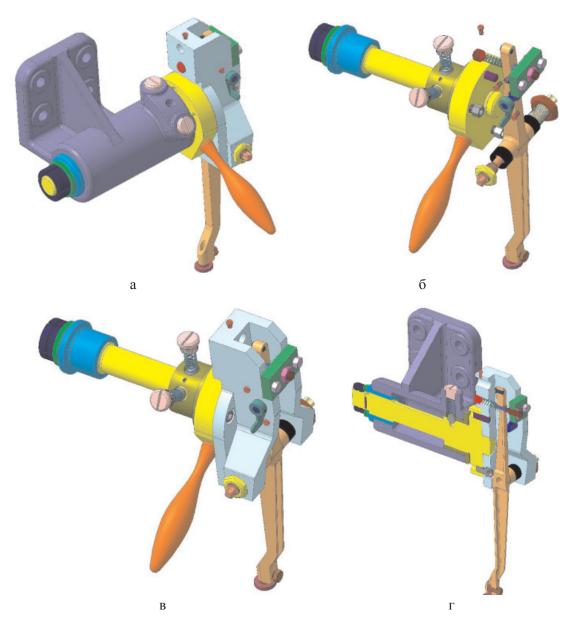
3D сборка приспособления для проверки биения торца блока шестерен
